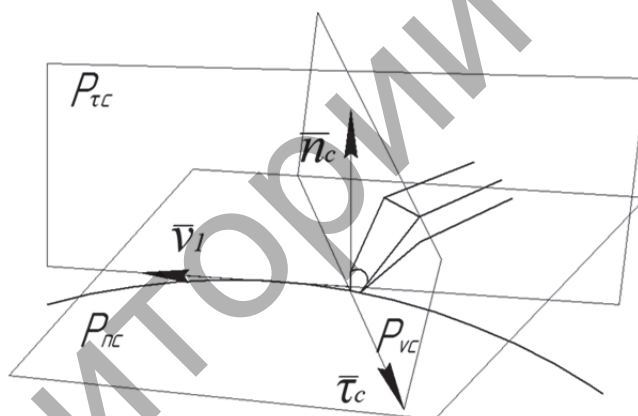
Положение инструмента на сферической поверхности в статической системе координат
